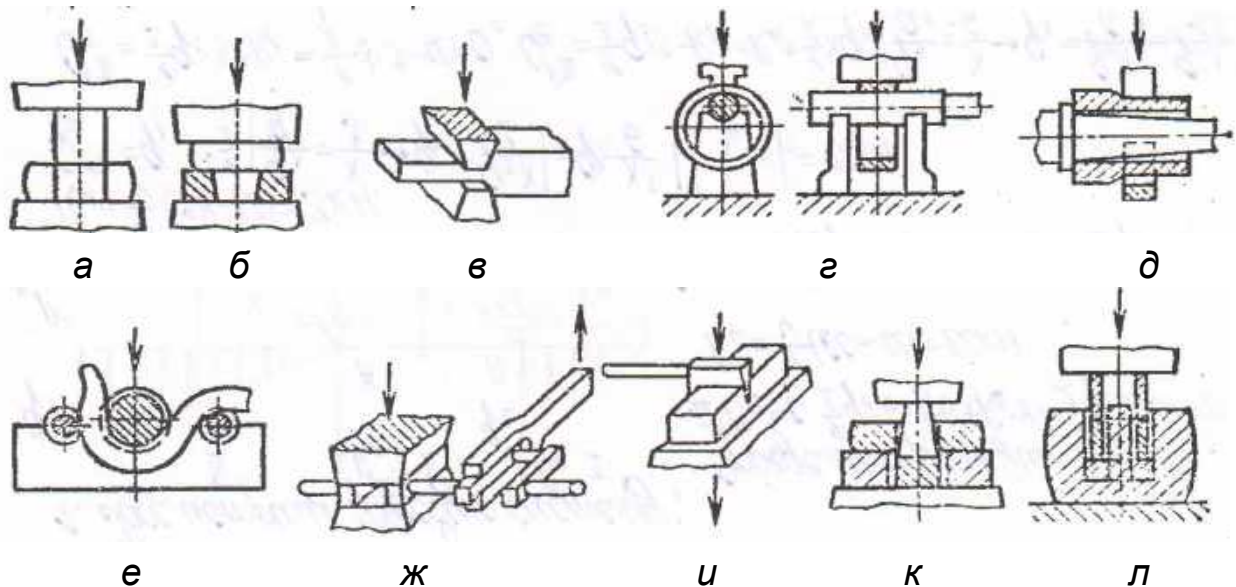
Схеми операцій вільного кування: а – осадка; б – висадка; в – витяжка; г – розкочування кілець; д – витяжка трубної заготовки; е – гнуття; ж – закручування; и – рубання; к – вирубування; л – прошивка
